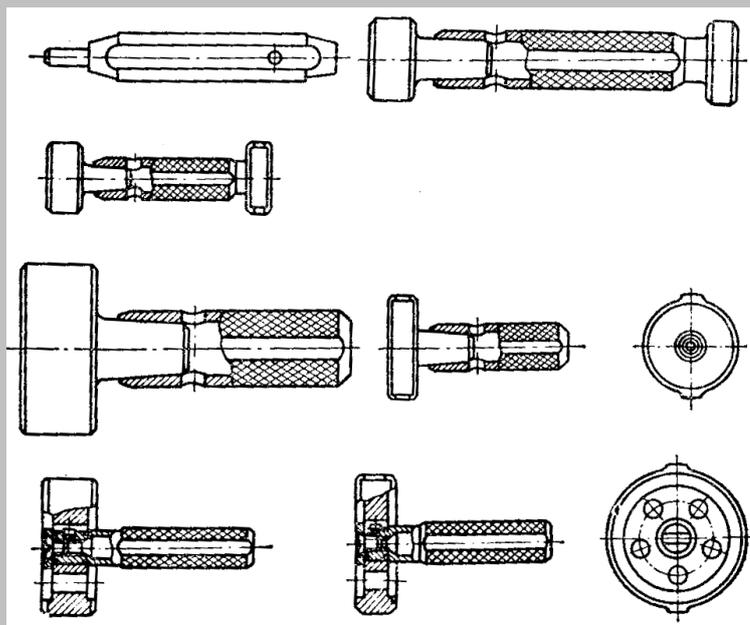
Гладкие калибры-пробки и их конструкции
